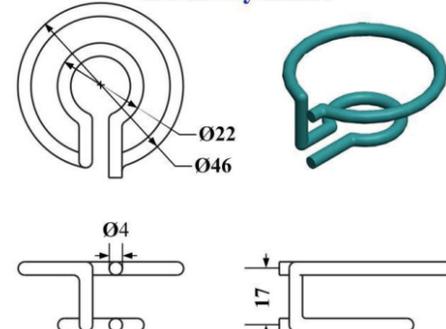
公模仁與母模仁內部之異形冷卻水路 3D CAD 模型與幾何尺寸 Unit: mm
